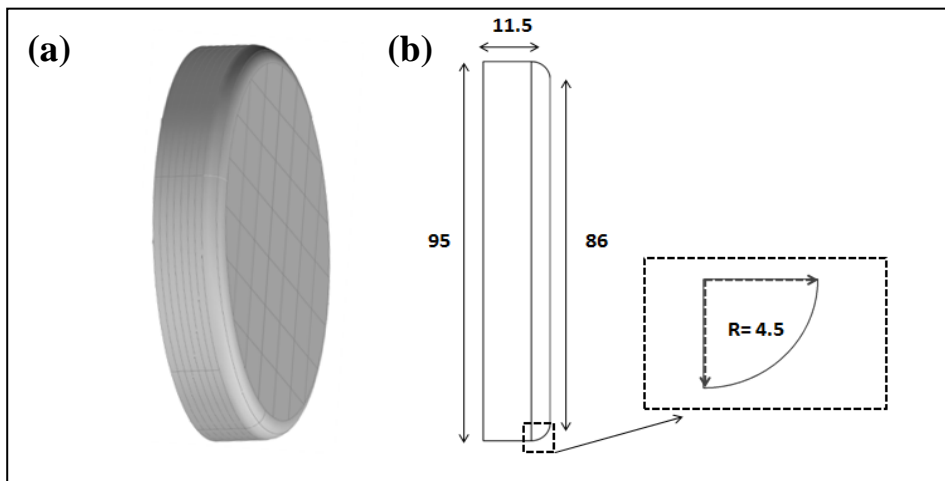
Galette cylindrique : vue 3D (a) et dimensions en mm (b).
